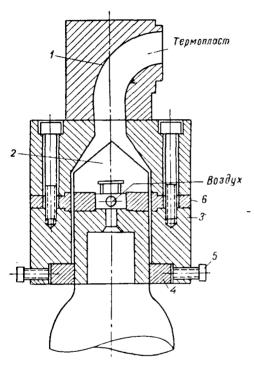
Головка с верхним питанием: I—труба для питания; 2—дорн; 3—корпус головки; 4—формующее кольцо; 5—регулировочный болт; 6—дорнодержатель.
